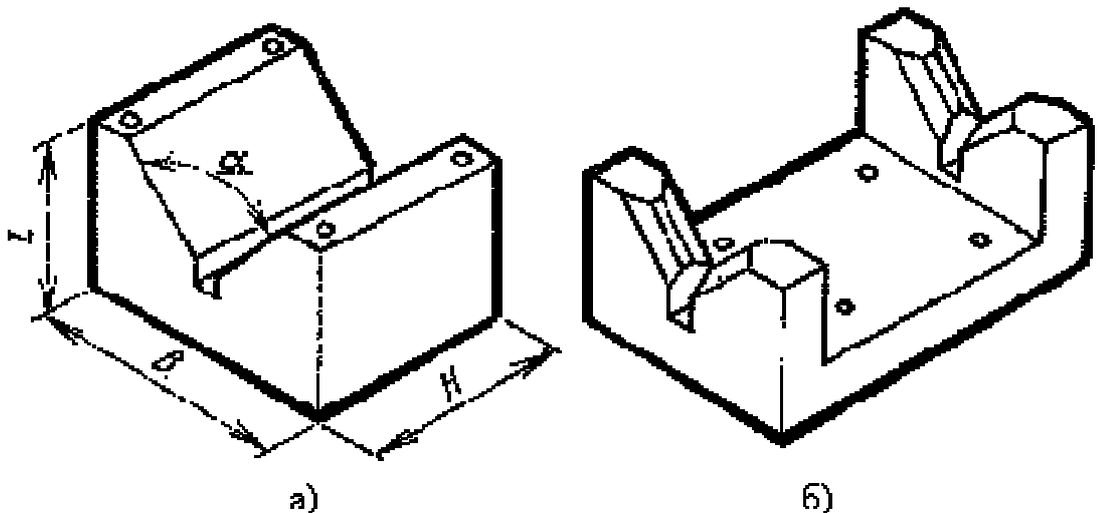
Элементы для установки заготовок по наружным и внутренним цилиндрическим поверхностям: а, б – призмы широкая и узкая сдвоенная
